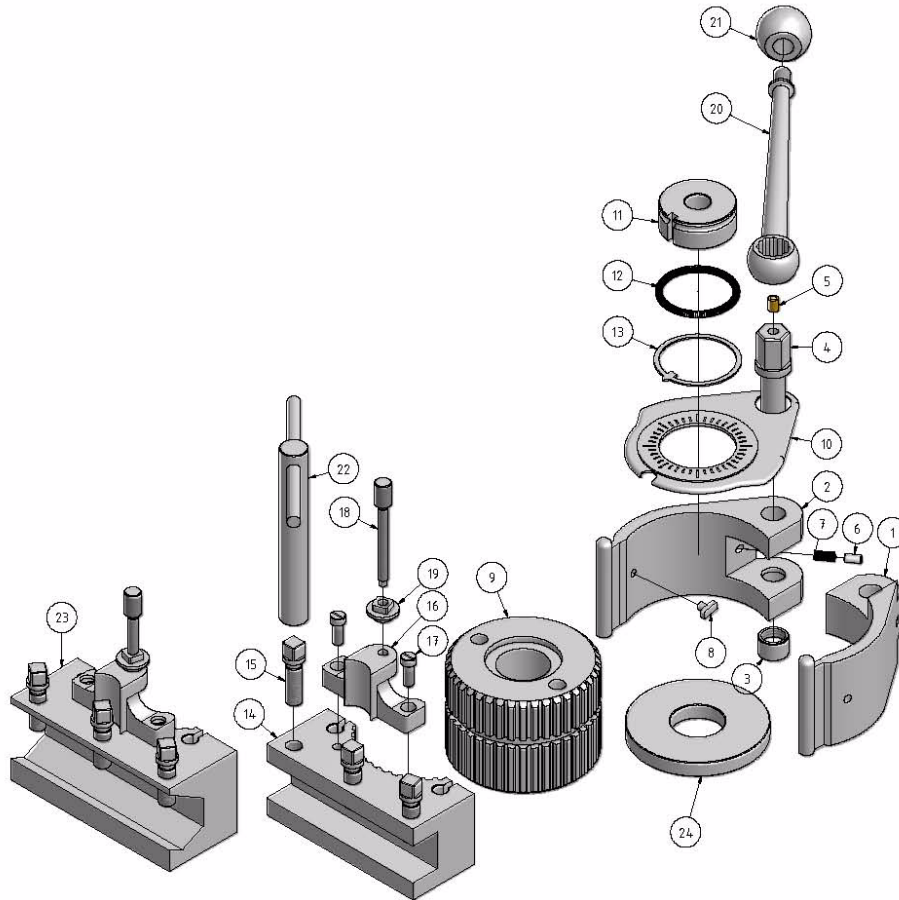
Ersatzteilzeichnung SWH 5-B/ 7-C - Drawing spare parts SWH 5-B/ 7-C
